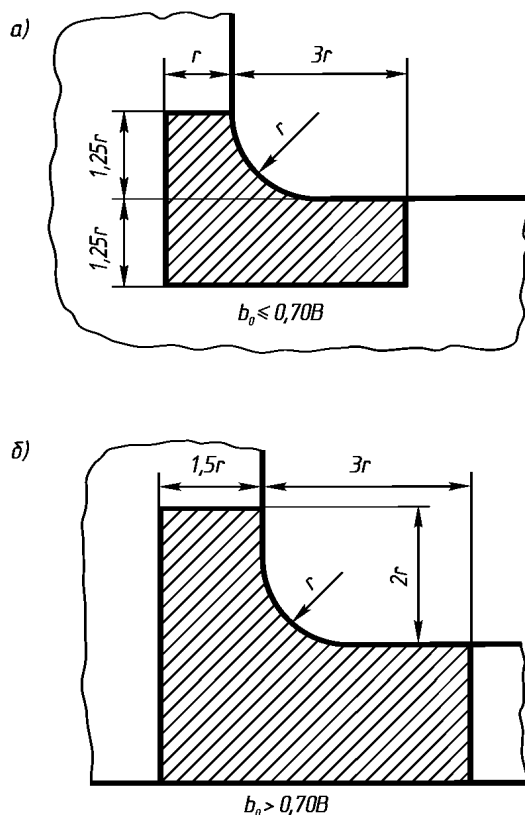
Участки палубы, в которых не допускается располагать стыковые швы
